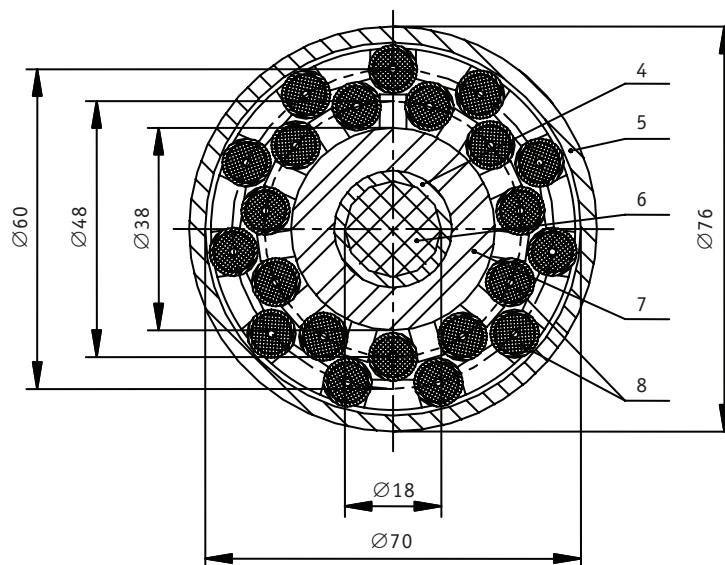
Поперечный разрез ТК реактора ИВГ1.2М в районе активной зоны: 4 – труба для установки поглотителя нейтронов; 5 – корпус ТК; 6 – поглотитель нейтронов; 7 – бериллиевый вытеснитель; 8 – твэл
